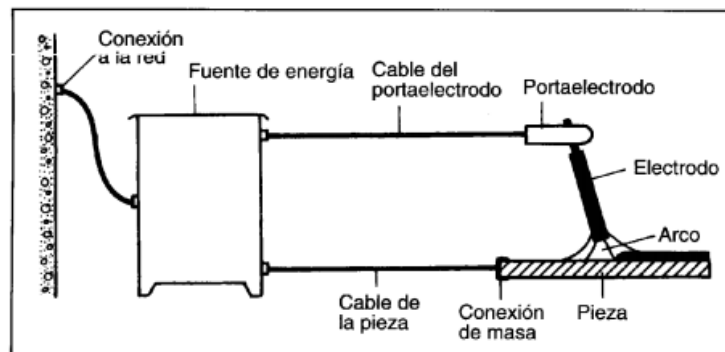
Equip de soldadura per arc amb elèctrode revestit. Apunts Tecnologia Mecànica.
